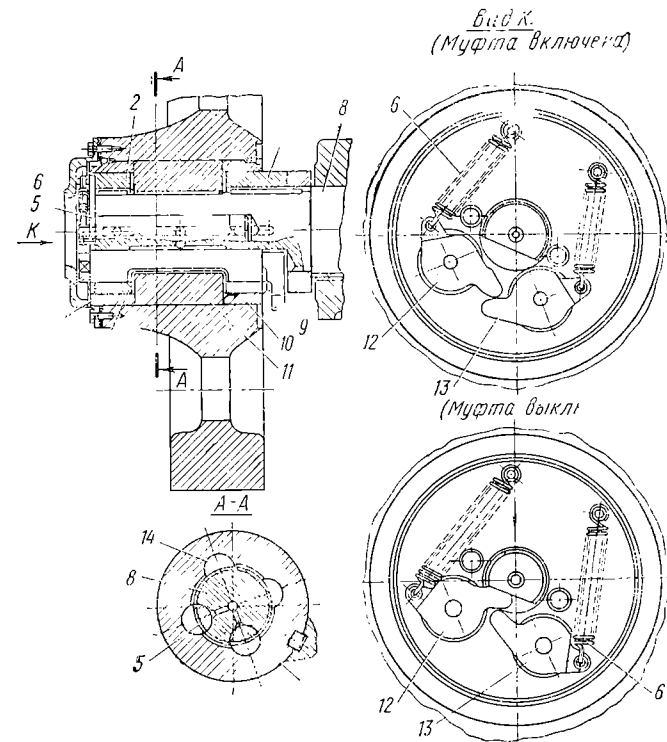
Жесткая муфта сцепления с двумя поворотными шпонками
